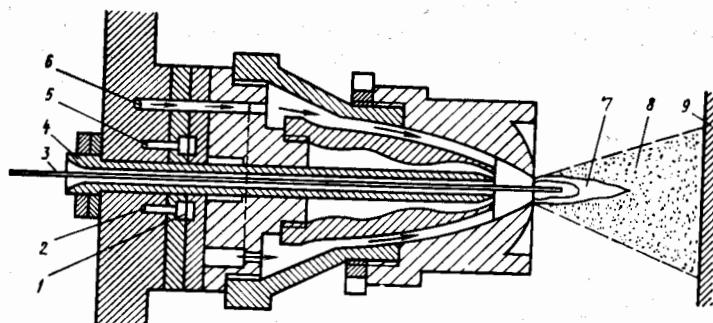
Распылительная головка аппарата для газопламенного напыления:
